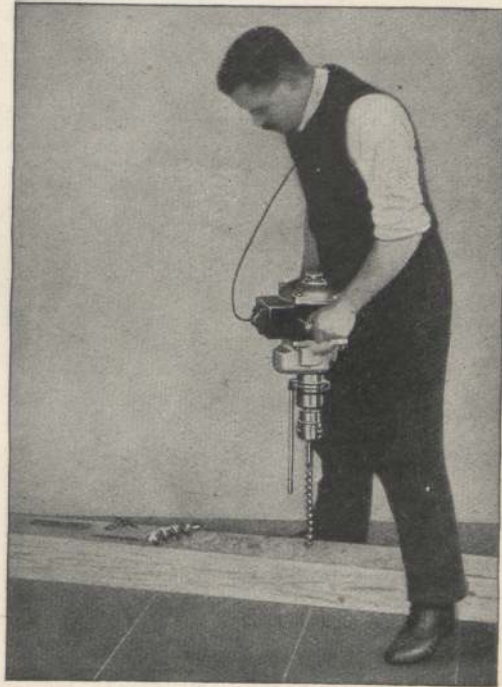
Die „Mafell“ als elektrische Bohrmaschine. Der aus seinem Fahrgestell (s. Abb. 1047) herausgenommene Motor kann als Handbohrmaschine benützt werden. Die Bohrlöcher kann man bis zu 80 mm Durchmesser und 1,00 m Tiefe ausführen. Der Motor hat ein Übersetzungsgetriebe, so daß er beim Bohren nur etwa 500 Umdrehungen pro Minute macht.
